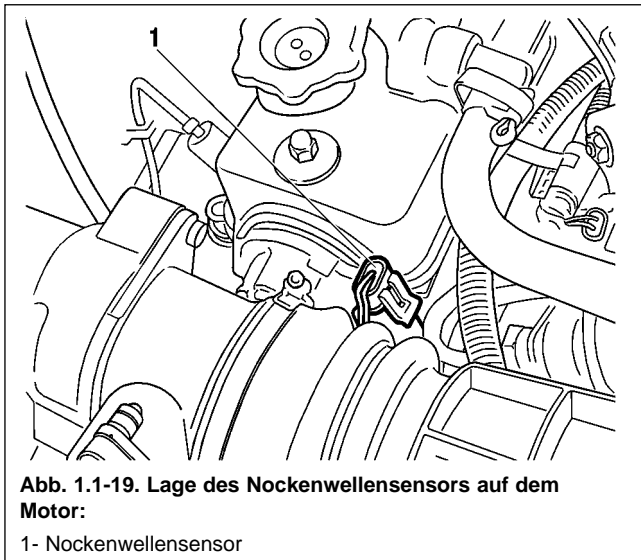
Lage des Nockenwellensensors auf dem Motor:
